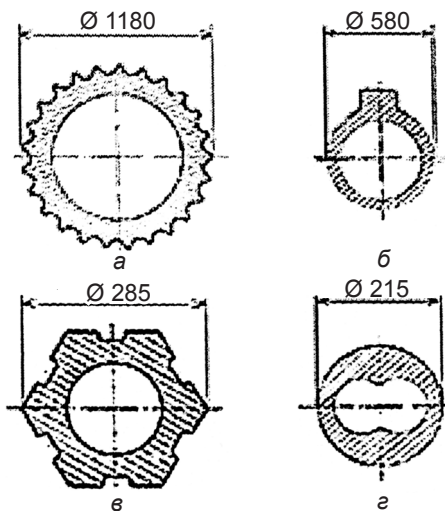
Форма поперечного сечения фасонных электрошлаковых заготовок: ведущего колеса трактора (а); эксцентрично расположенная полость и прямоугольный выступ снаружи стенки (б); продольного суппорта станка-автомата (в); корпуса двухчервячного гранулятора (г)
